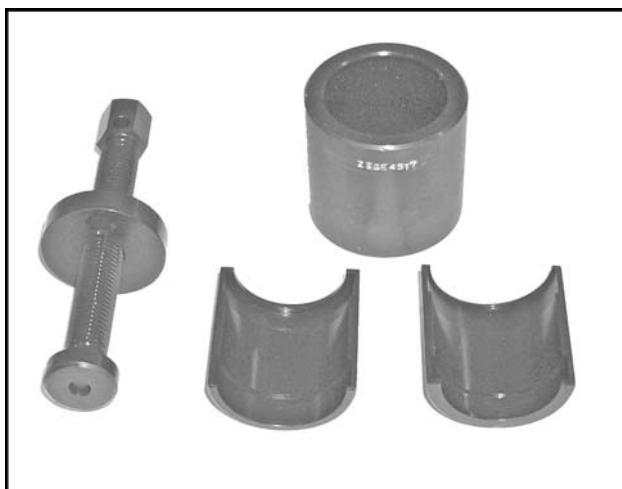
Extractor de camisa de desgaste delantera, ZTSE4517
